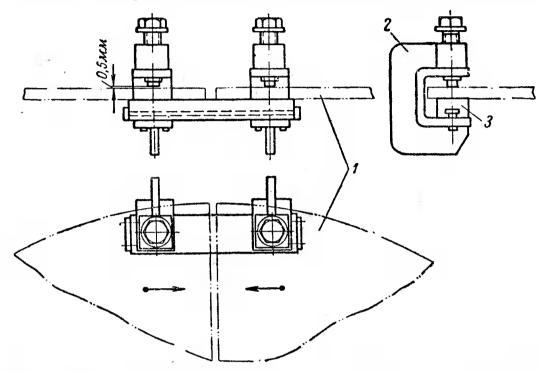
Приспособление для направления опорных полок ярмовых балок во время прессовки магнитопровода.
